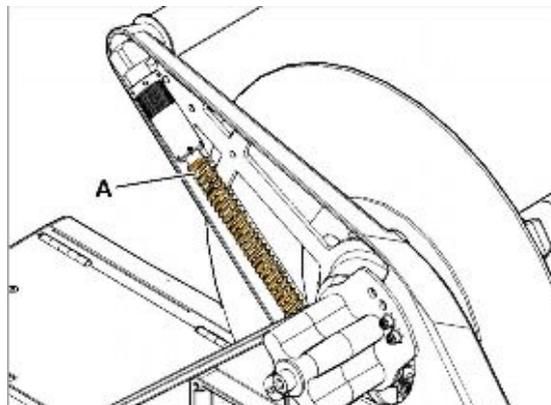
Пружина (А) плавающего рычага на 400-мм размотчике
